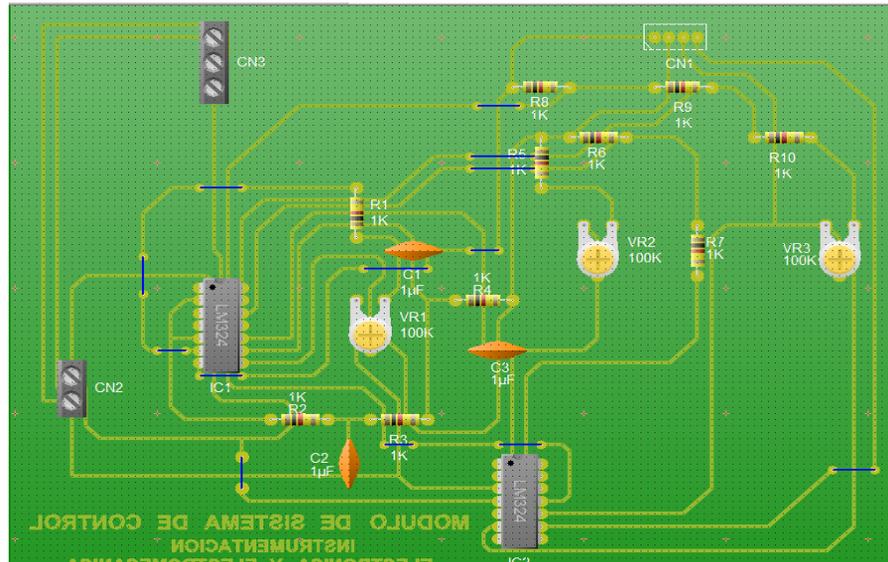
a Diseño del módulo de sistemas de control en PCB WIZARD
